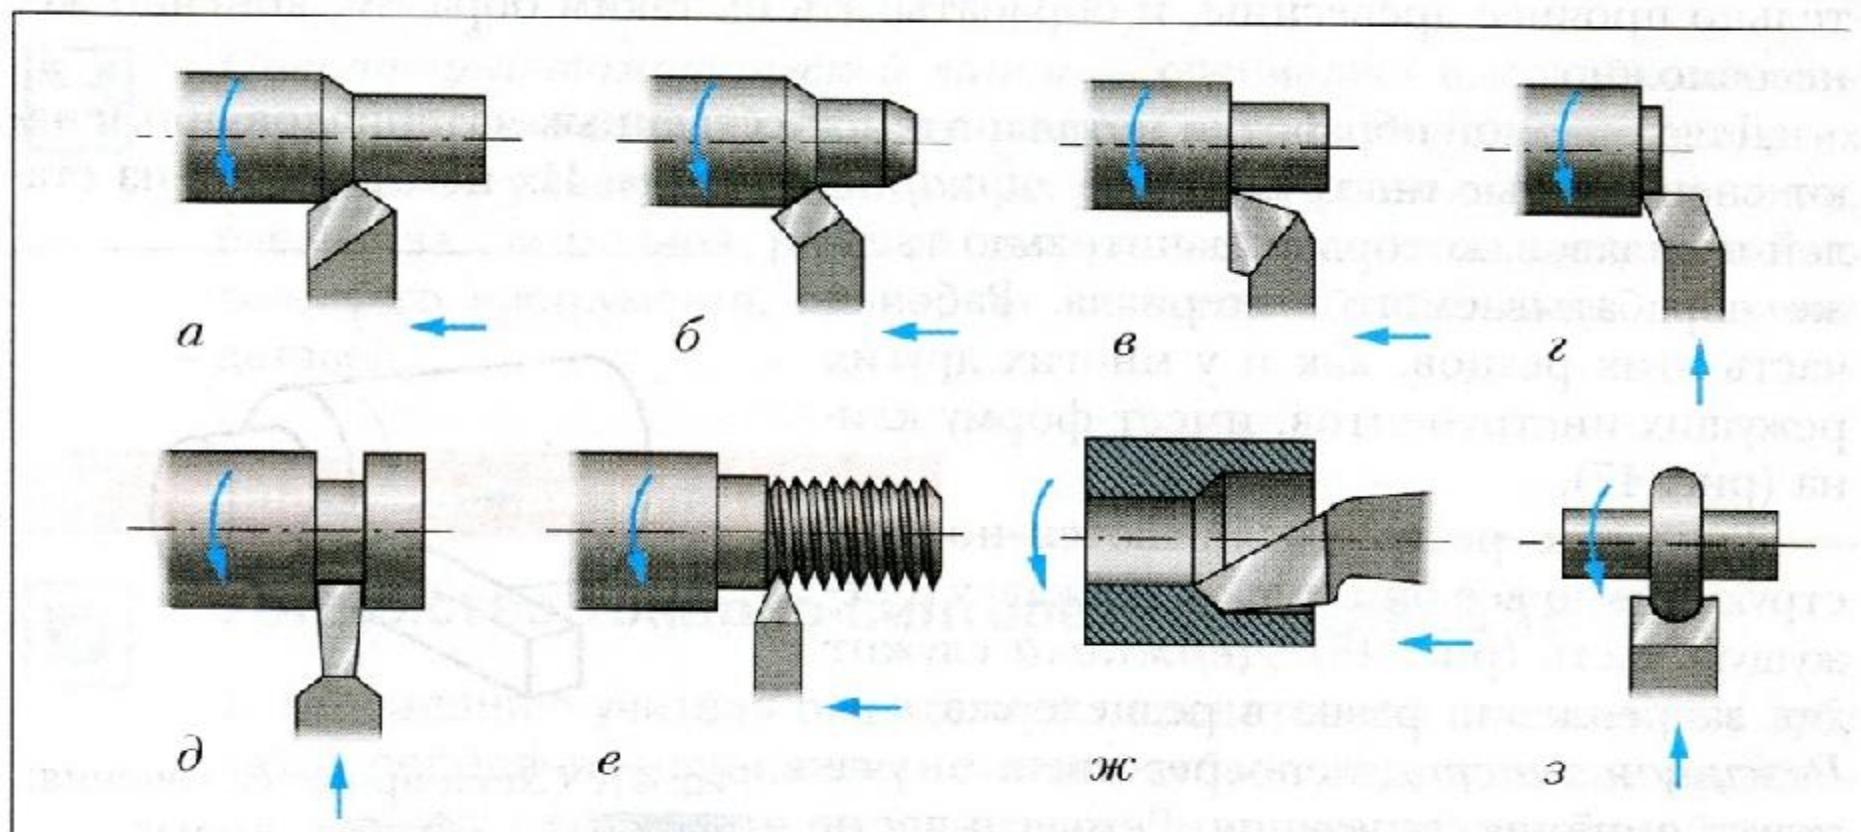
Токарные резцы: *а* — проходной прямой; *б* — проходной отогнутый; *в* — проходной упорный; *г* — подрезной; *д* — отрезной; *е* — резьбовой; *ж* — проходной расточкой; *з* — фасонный
